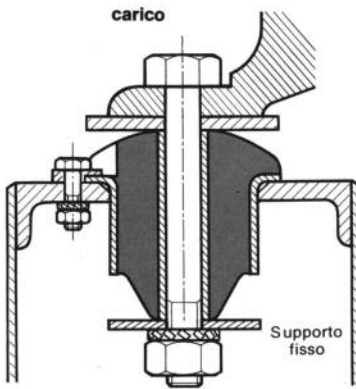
Montaggio ai piedi della macchina e chassis metallico
